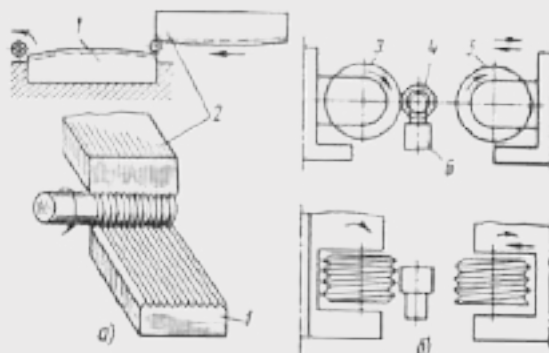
Накочення різьби: а) плоскими плашками; б) круглими плашками-роликами; 1, 2 — плоскі плашки; 3, 5 — ролики; 4 — деталь; 6 — підставка
